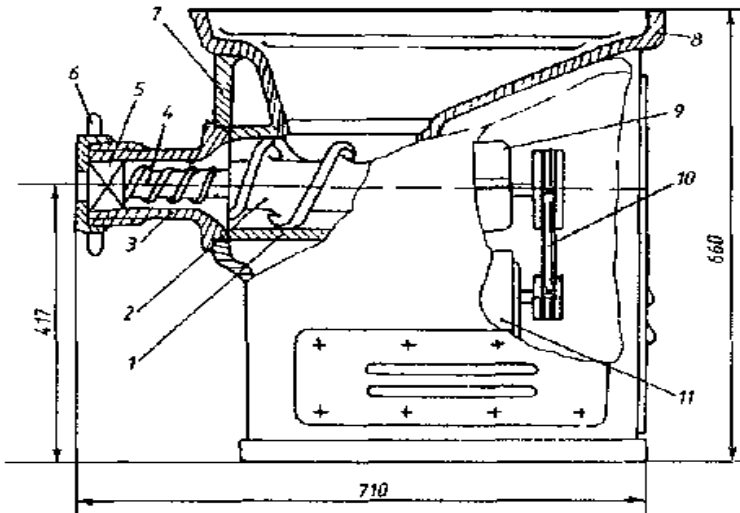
Вовчок МП-82: 1 - корпус живильного шнека; 2 - живильний шнек; 3 - циліндричний корпус подавального шнека; 4 - подавальний шнек; 5 - ріжучий механізм; 6 - накидна гайка; 7 - станина; 8 - завантажувальна горловина; 9 - редуктор; 10 - клинопасова передача; 11 - електродвигун
